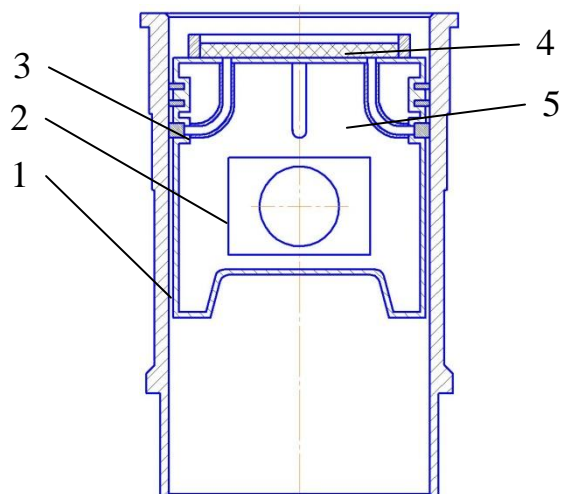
Схема смазывания рабочей поверхности гильзы цилиндра
